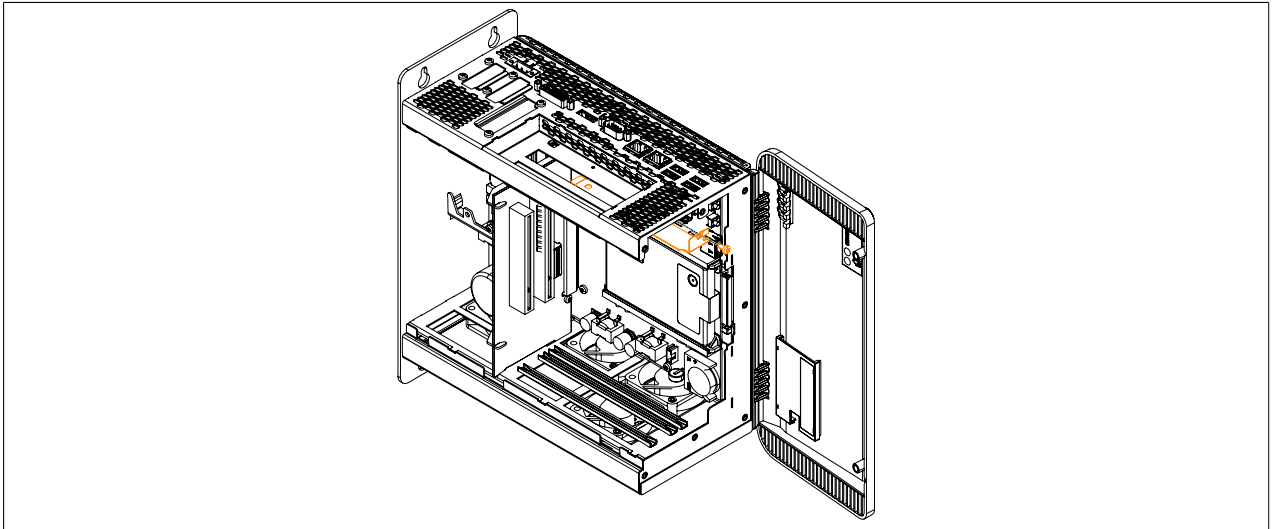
PCI / PCIe Blindabdeckung entfernen
